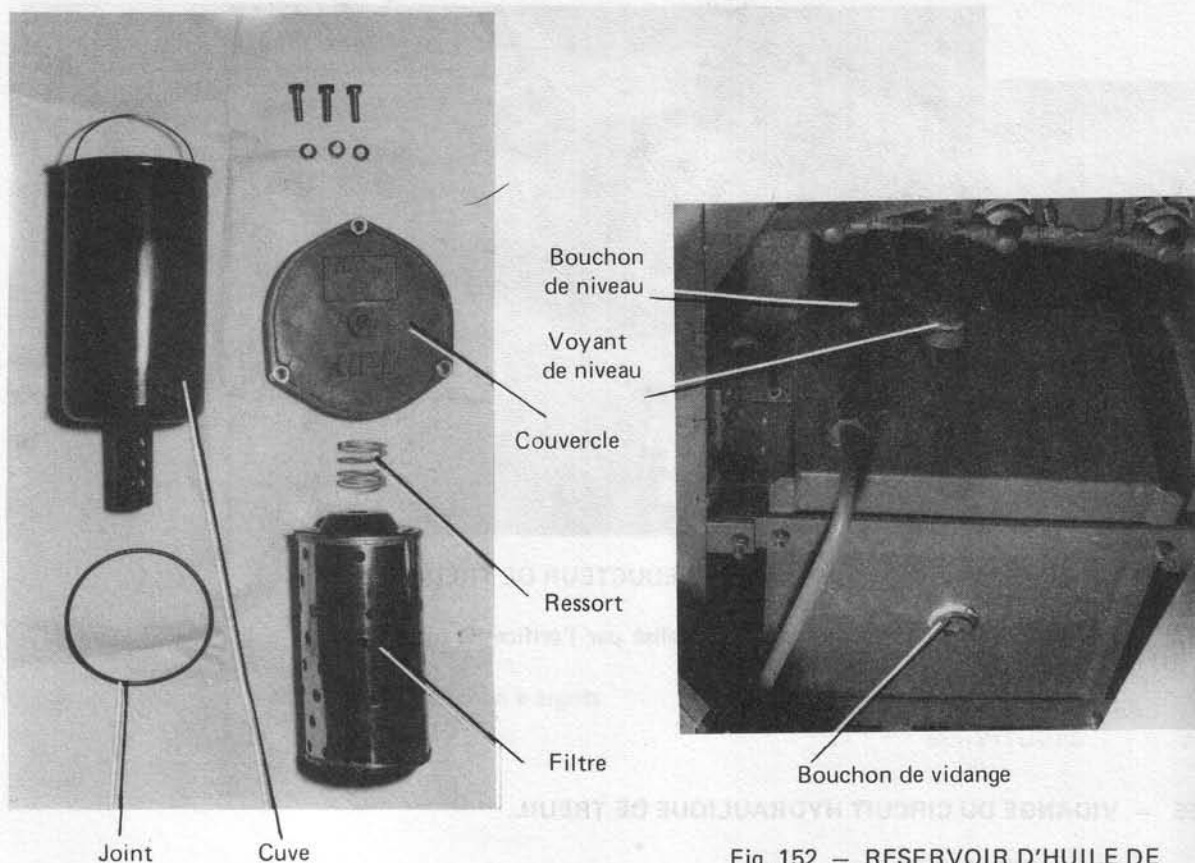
VUE ECLATEE DU FILTRE DE CIRCUIT HYDRAULIQUE DE TREUIL.
